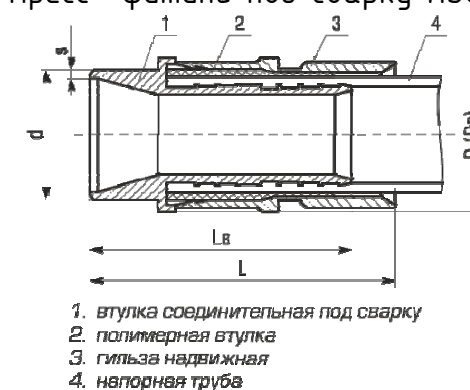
Пресс-фитинг под сварку ИЗОПРОФЛЕКС-115А
